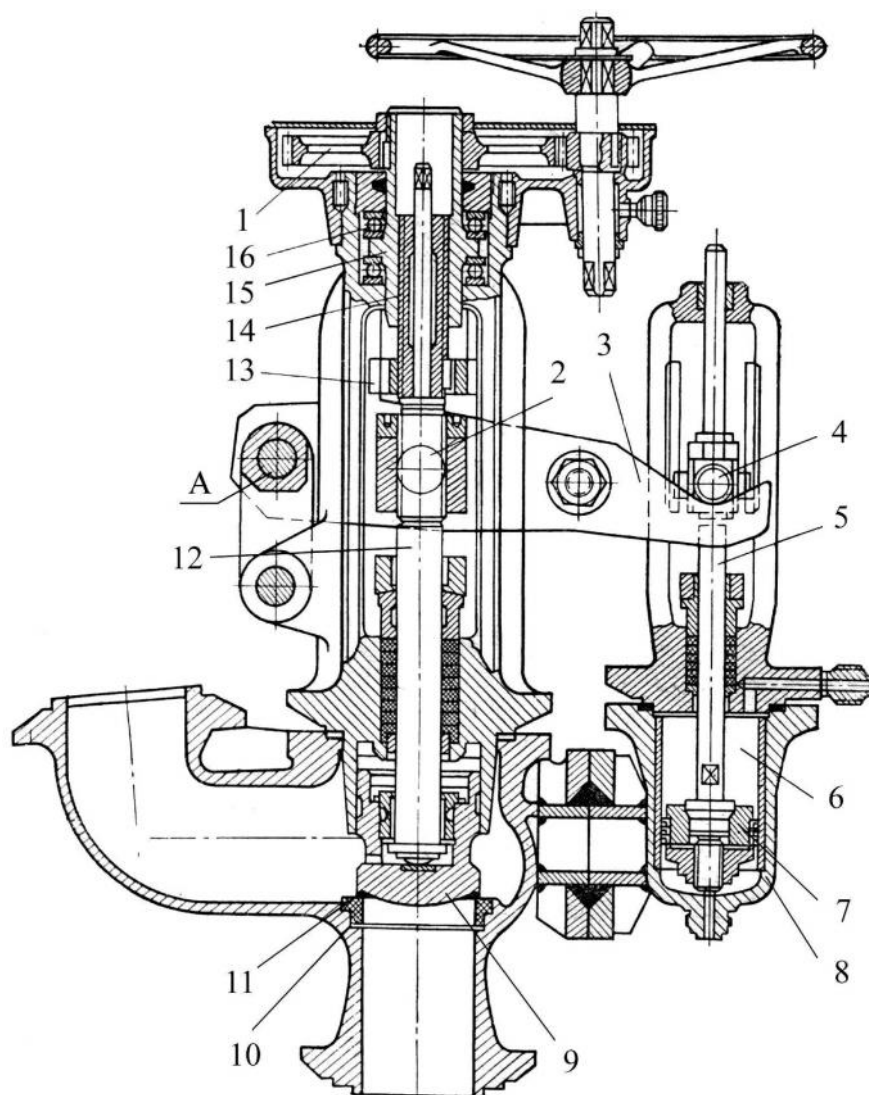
Быстрозапорный стопорный клапан: 1 – зубчатая передача; 2 – поперечина; 3 – рычаг; 4 – крестовина; 5, 12 – шток; 6 – сервомотор; 7 – поршень; 8 – цилиндр; 9 – тарелка; 10 – гнездо; 11 – седло; 13 – стопор; 14 – втулка; 15 – гайка; 16 – подшипник
